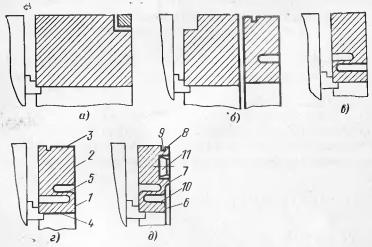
Изготовление Z-образного центрирующего кольца на токарном станке.
